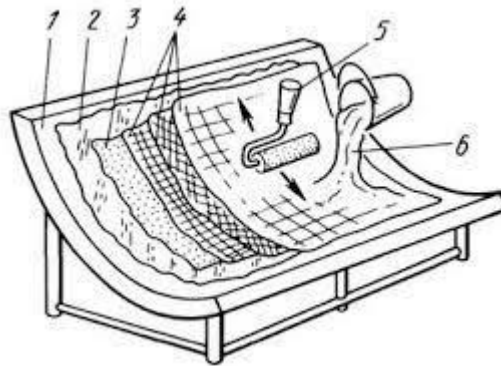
Елементи конструкції форми та виробу при формуванні ручною викладкою: 1 – форма; 2 – розділювальна плівка; 3 – зовнішній смоляний шар; 4 – скловолокно; 5 – ручний валик; 6 – смола в суміші з каталізатором
